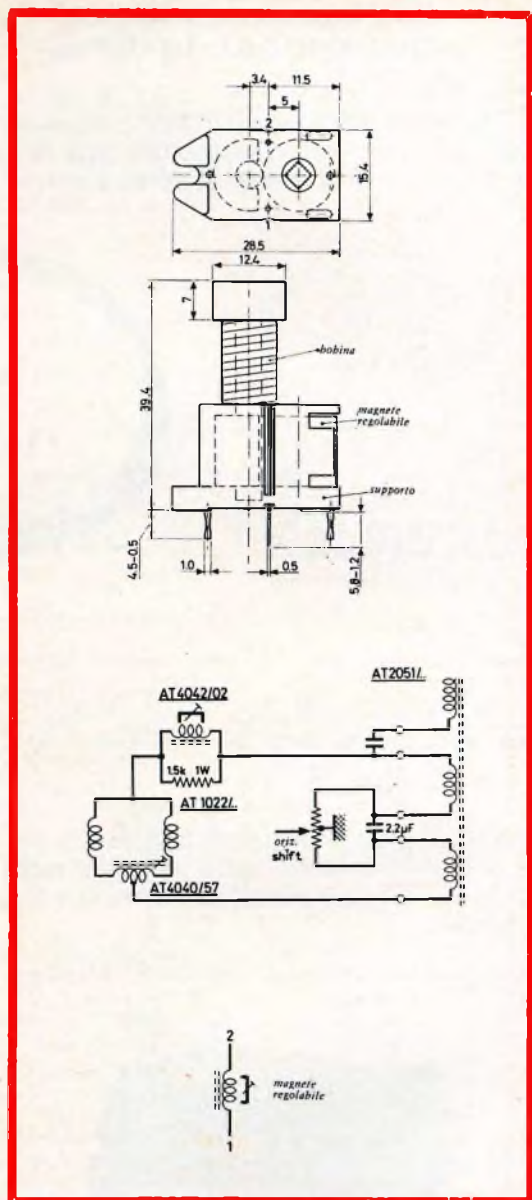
Dimensioni d'ingombro e collegamenti del regolatore di linearità AT 4042/02.
